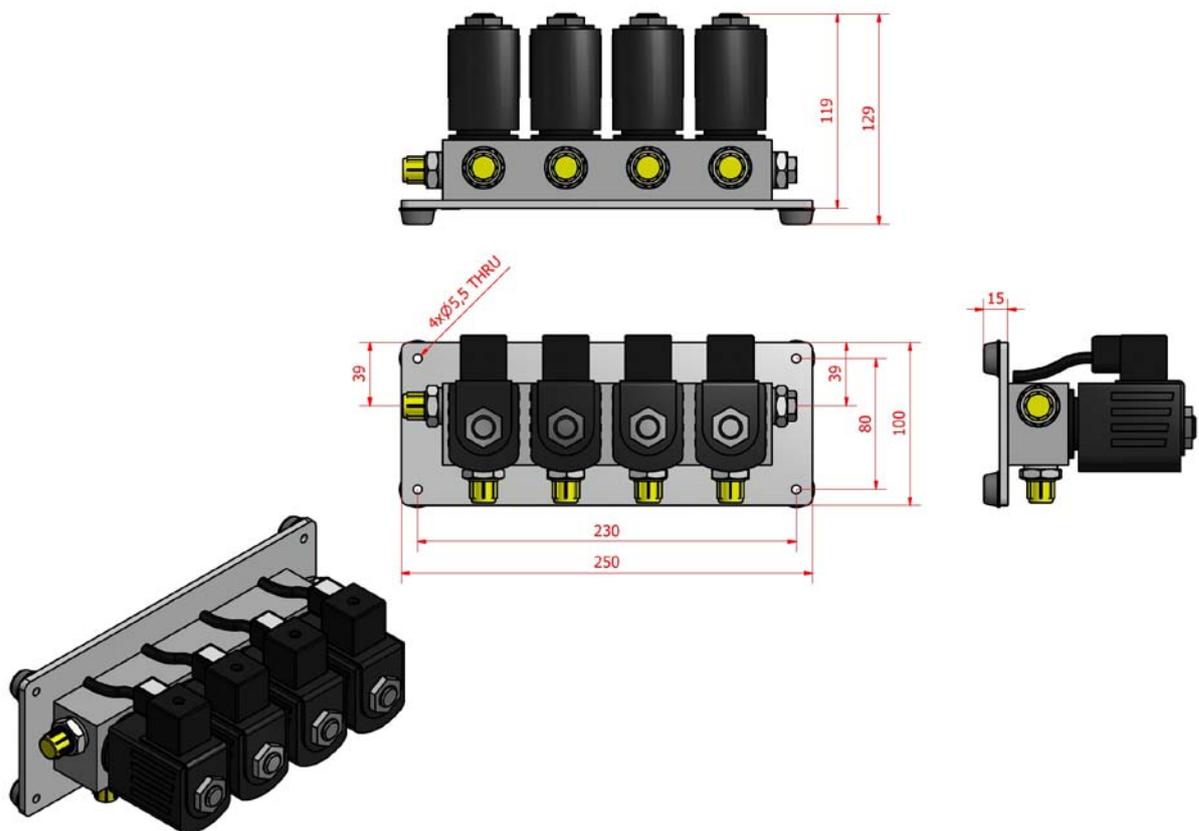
Dimensions du bloc de vannes 3+1 INDUCT (en mm)
